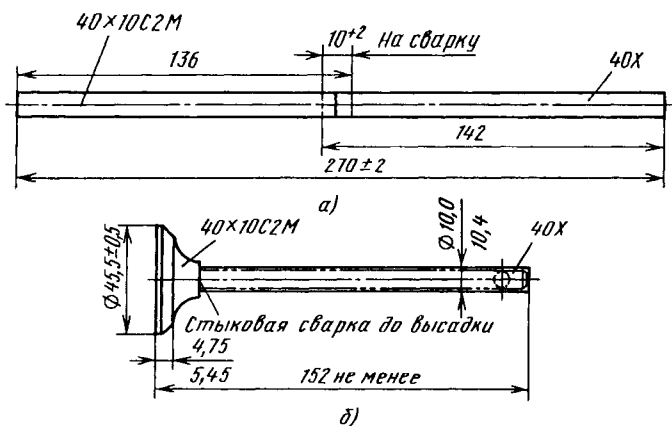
Заготовка клапана (а) и готовая деталь (б) из двух различных материалов, соединенных стыковой сваркой
